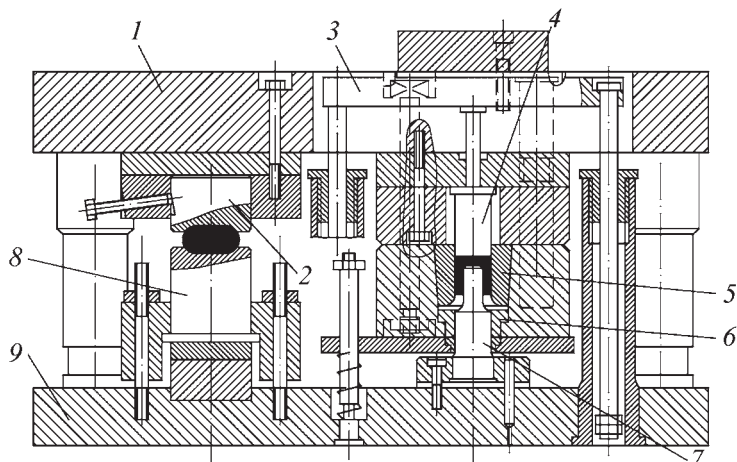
Штамп для полугорячего выдавливания корпуса подшипника хлопкоуборочной машины:
